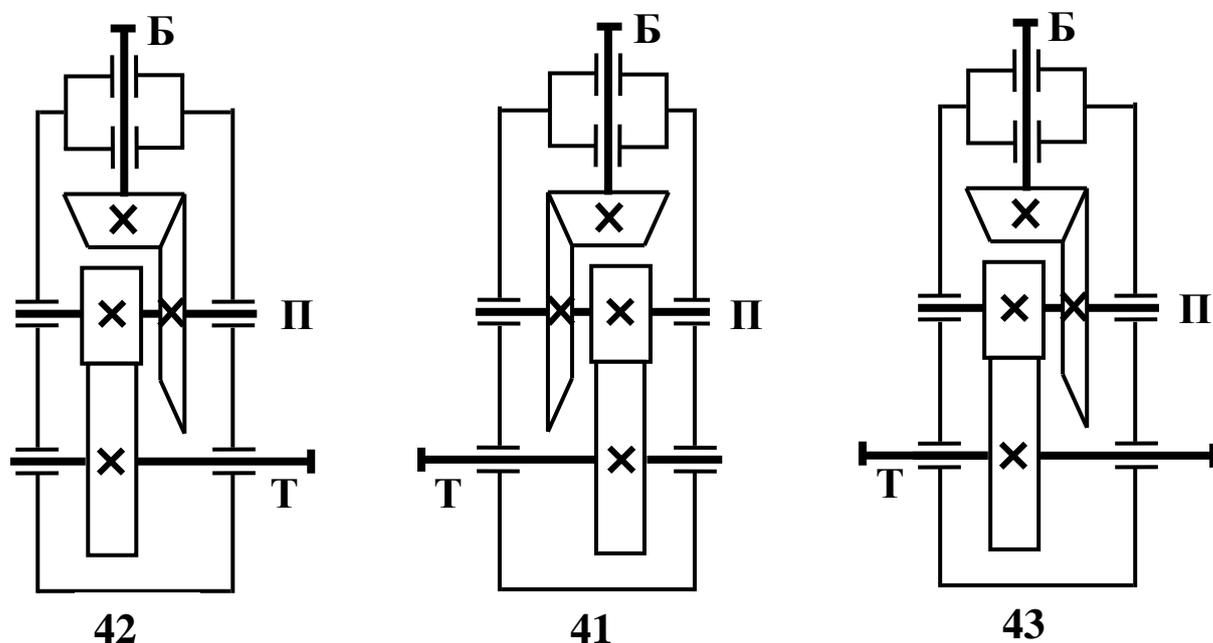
Основные схемы двухступенчатых коническо-цилиндрических редукторов
